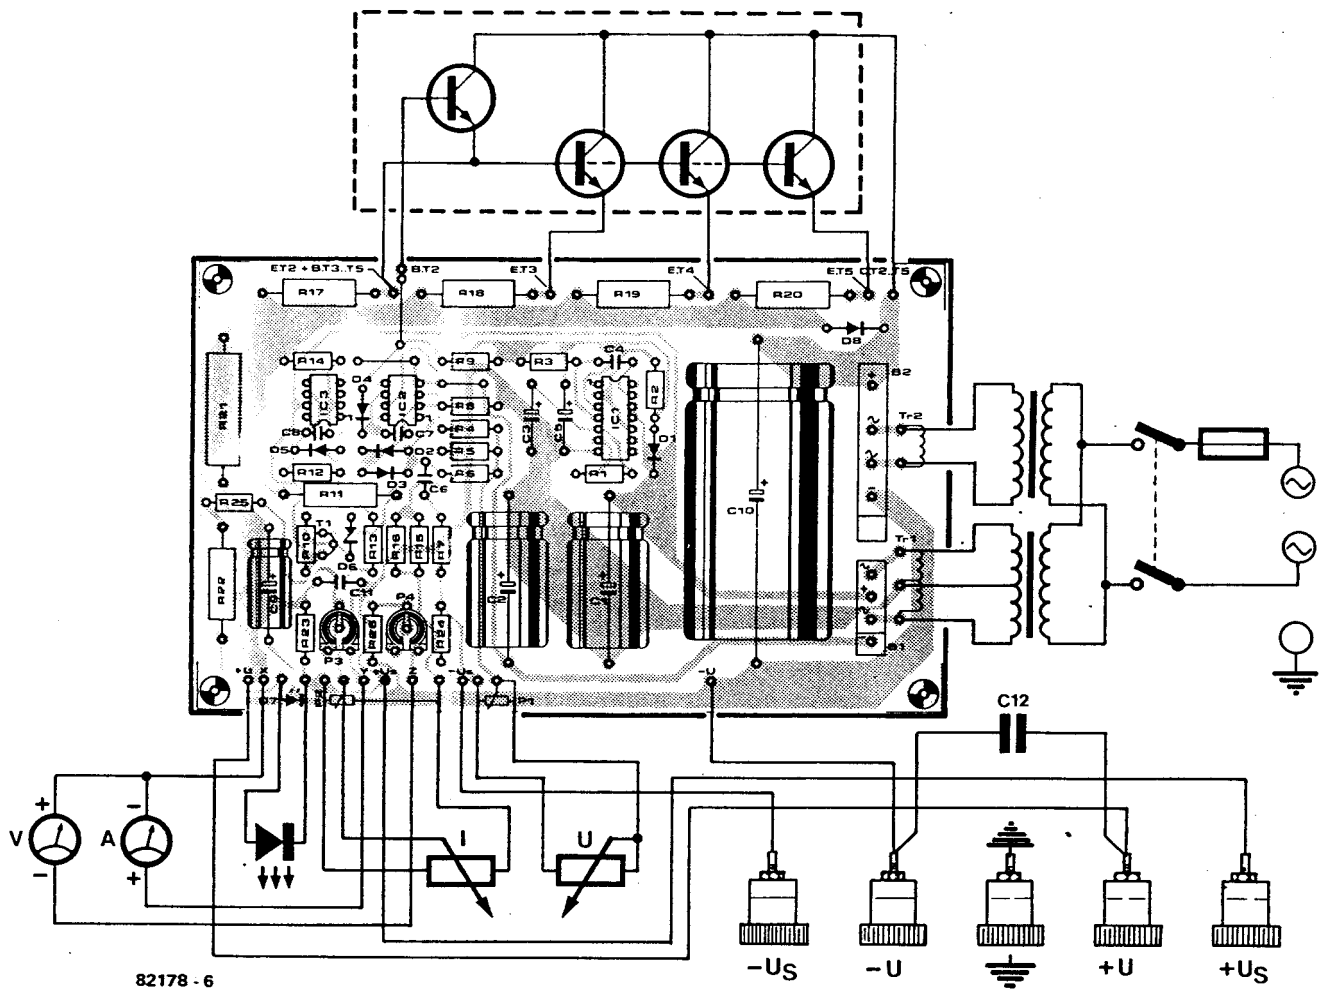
Mit Verdrahtungsplan geht alles leichter.
